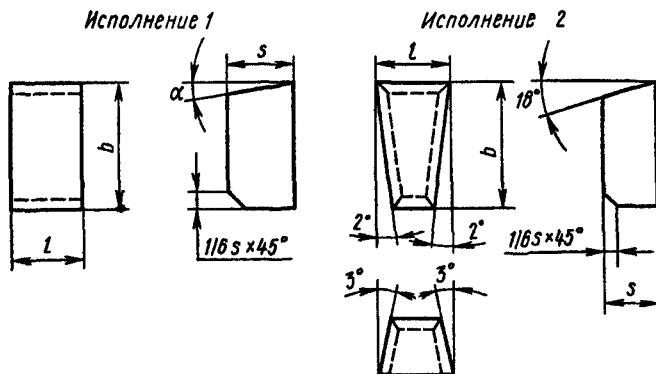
Формы напайных твердосплавных пластин для резцов
